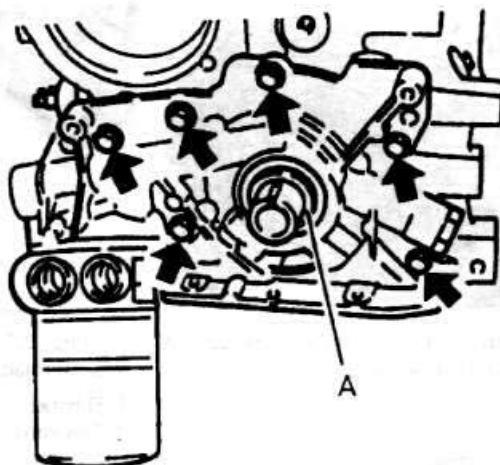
Болты маслонасоса (показаны стрелками) и прокладка коленчатого вала (А) — двигатель с двумя распредвалами
